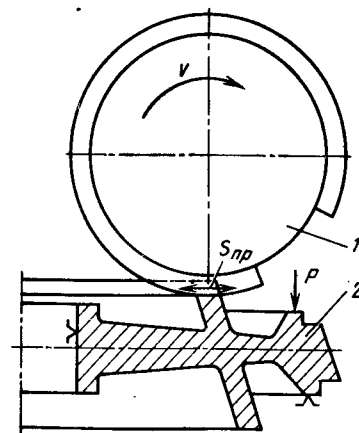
Схема кругового протягивания торцевых шлиц в дисках компрессора на шлицепротяжном полуавтомате типа ПШН
